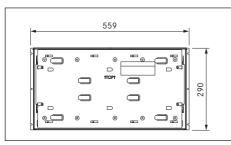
Dimensiones del aparato vista frontal MS290
